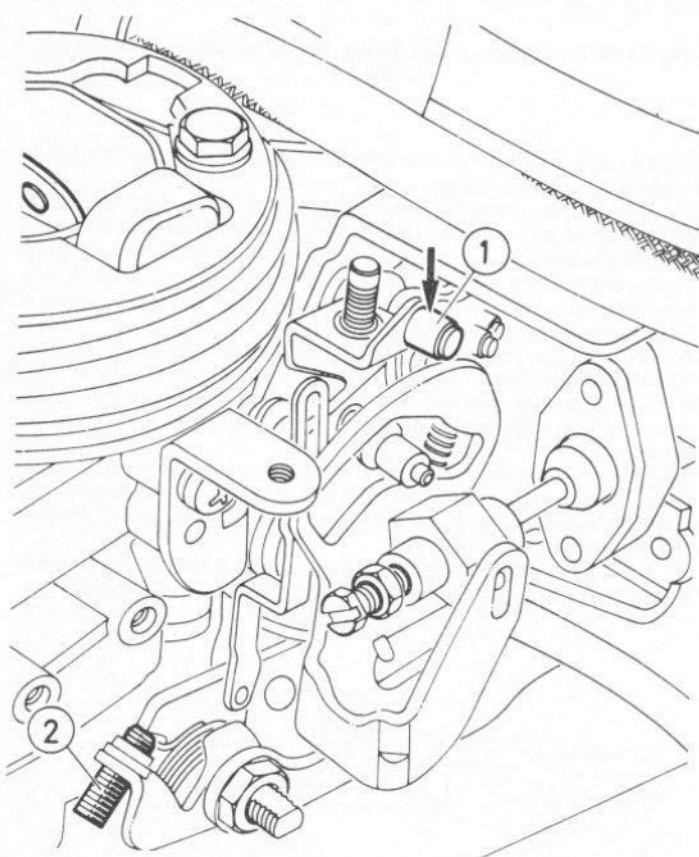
Réglage d'ouverture positive de papillon - carburateur Weber 36 TLC (Sec 8)
